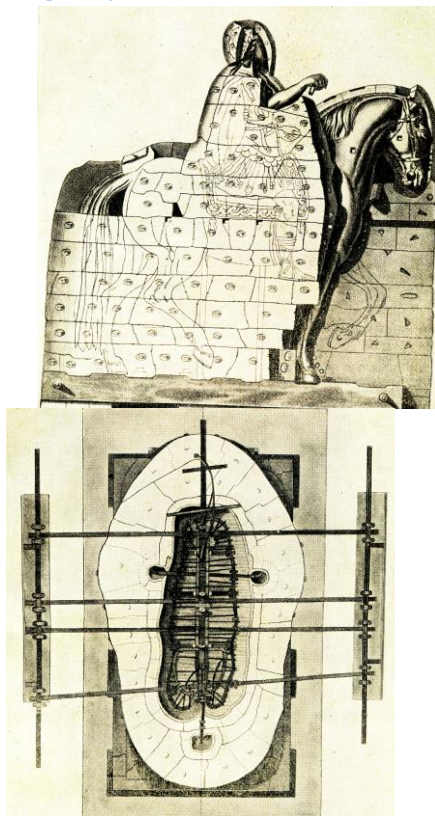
Вертикальный разрез кусковой формы (а) и горизонтальный разрез гипсовой формы с металлическим каркасом для крепления стержня (б)
